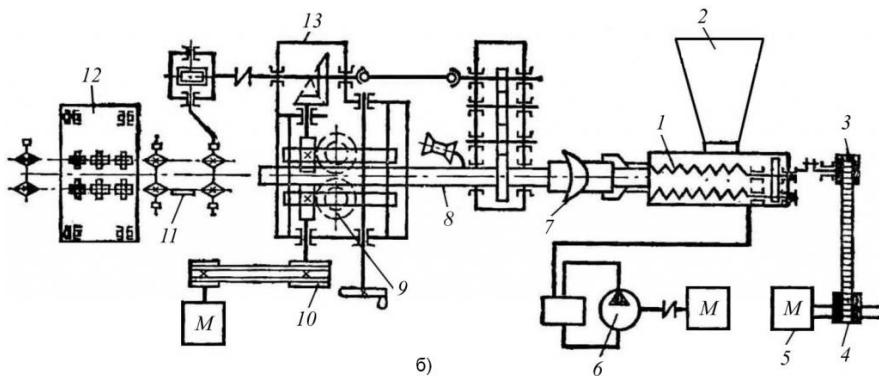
Агрегат Л5-ФАЛ для виробництва ковбасних виробів (кінематична схема): 1 - шнековий нагнітач; 2 - бункер; 3 - варіатор; 4 - шків; 5 - електродвигун; 6 - вакуум-насос; 7 - рукавоутворювач; 8 - цівка; 9 - гумові ролики; 10 - клинопасова передача; 11 - механізм знімання оболонки; 12 - механізм накладення скріпок; 13 - зубчасті колеса
